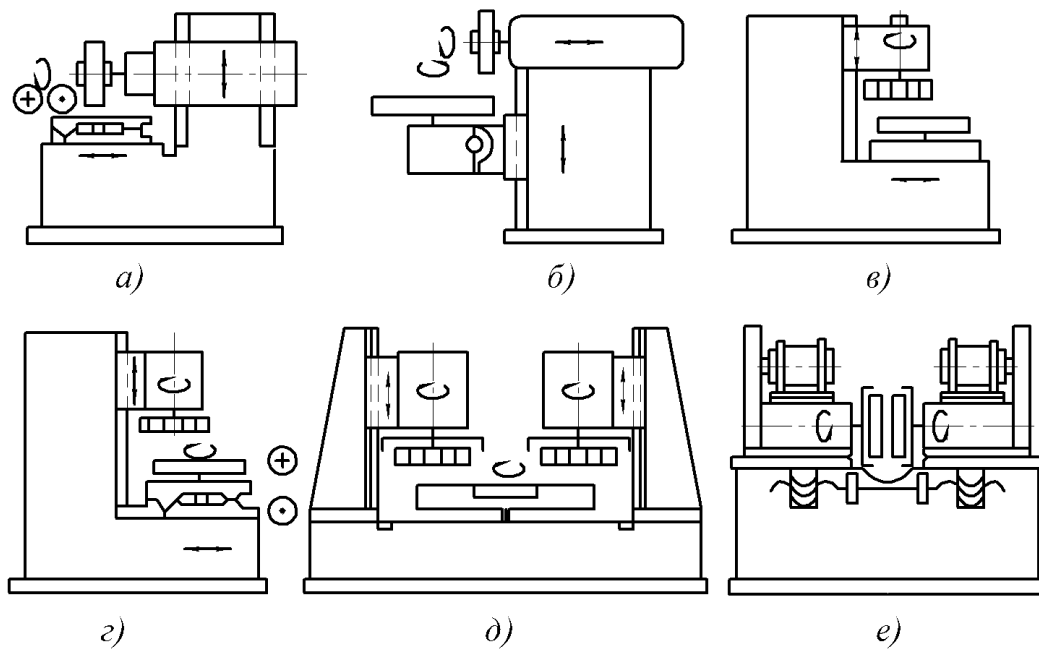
Схема оброблювання на плоскошліфувальних верстатах:
